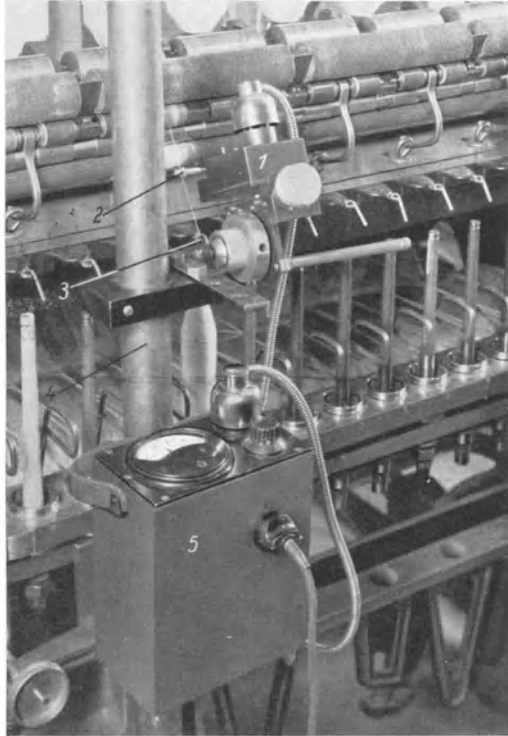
Siemens-Fadenspannungsmesser an einer Ringspinnmaschine.
